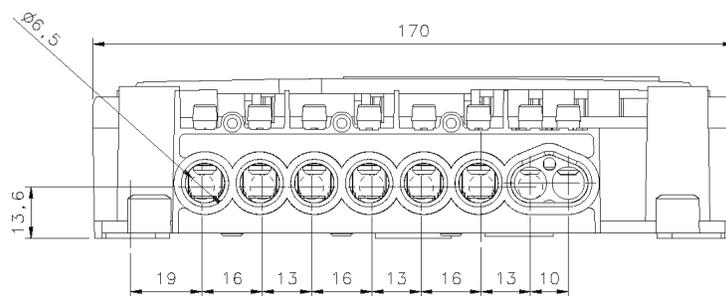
Disposición de bornes y dimensiones en vista inferior
